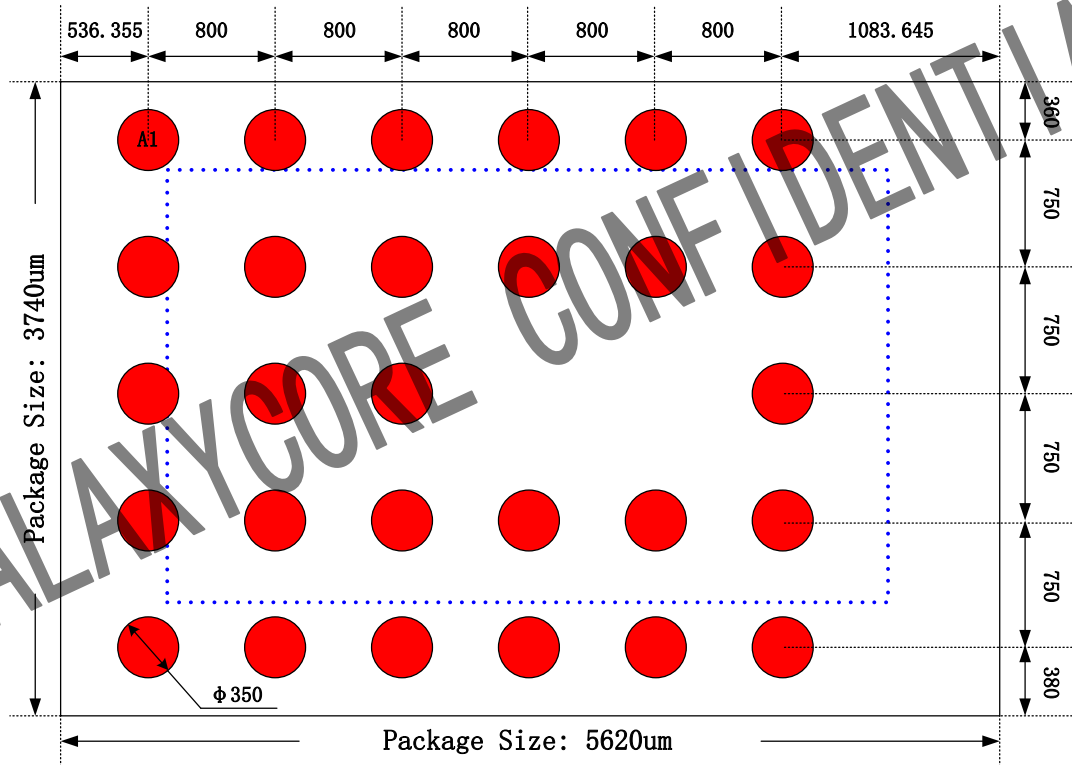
PCB 焊盘设计说明示意图(Top View)
